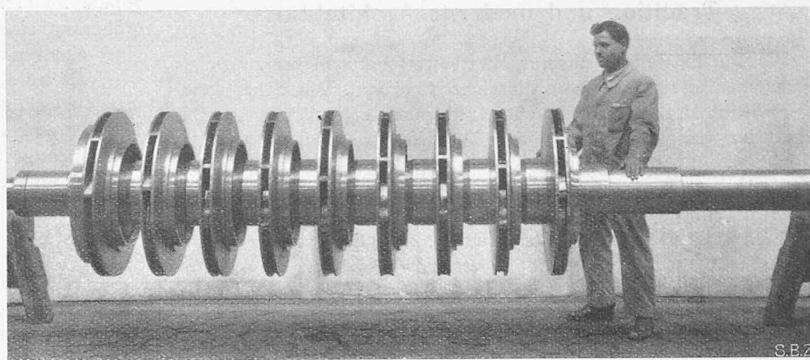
Rotor einer der Hochdruck-Pumpen.
